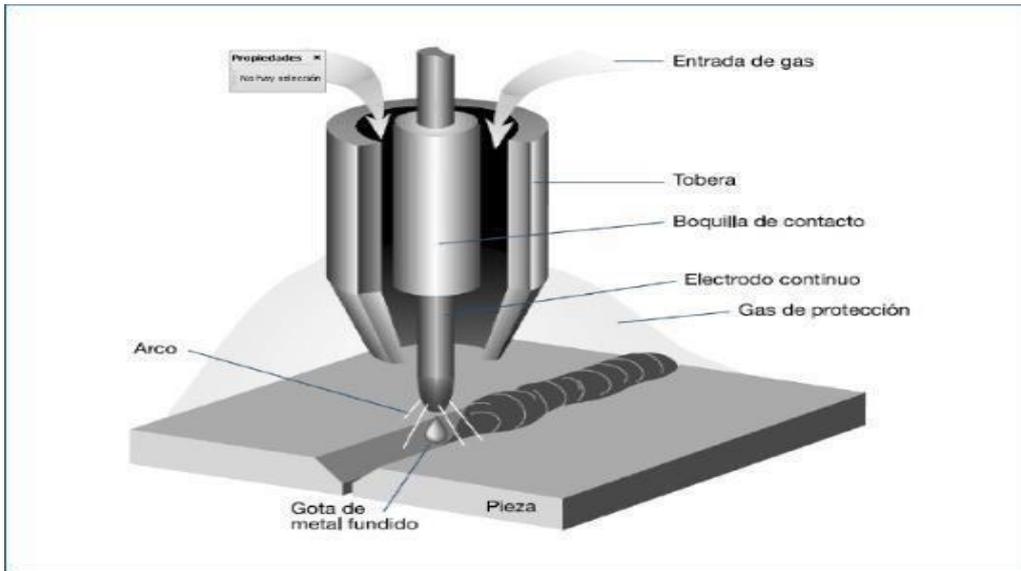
Proceso de soldadura Mig Mag – Gmaw.
